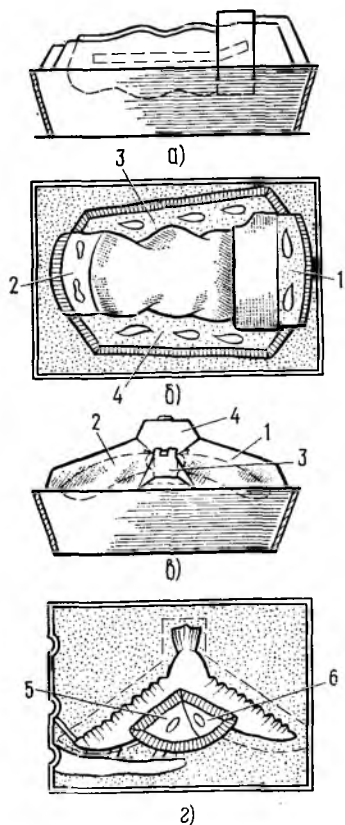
Процесс формовки статуэтки «Орел на скале»
